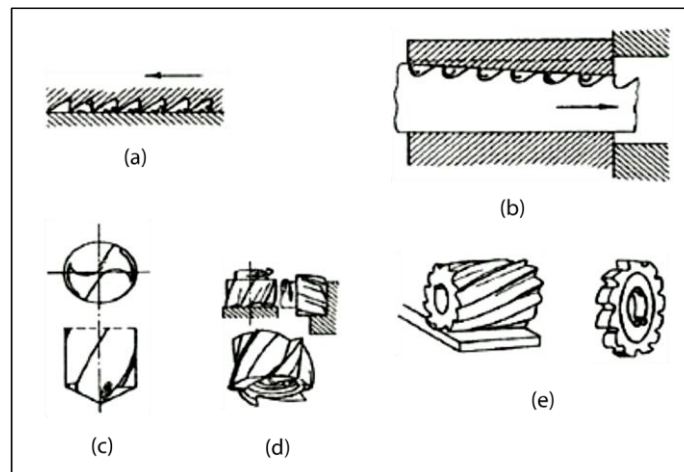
Ejemplos de herramientas de puntas múltiples, ilustrado de manera en la que la disposición geométrica de los filos permite diseñar cortadores de formas muy variadas
